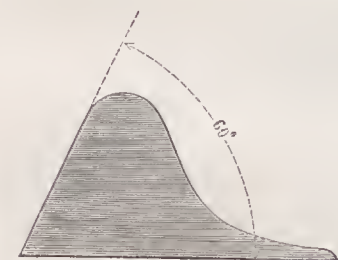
Sector de ebonita de la máquina de Bertsch
